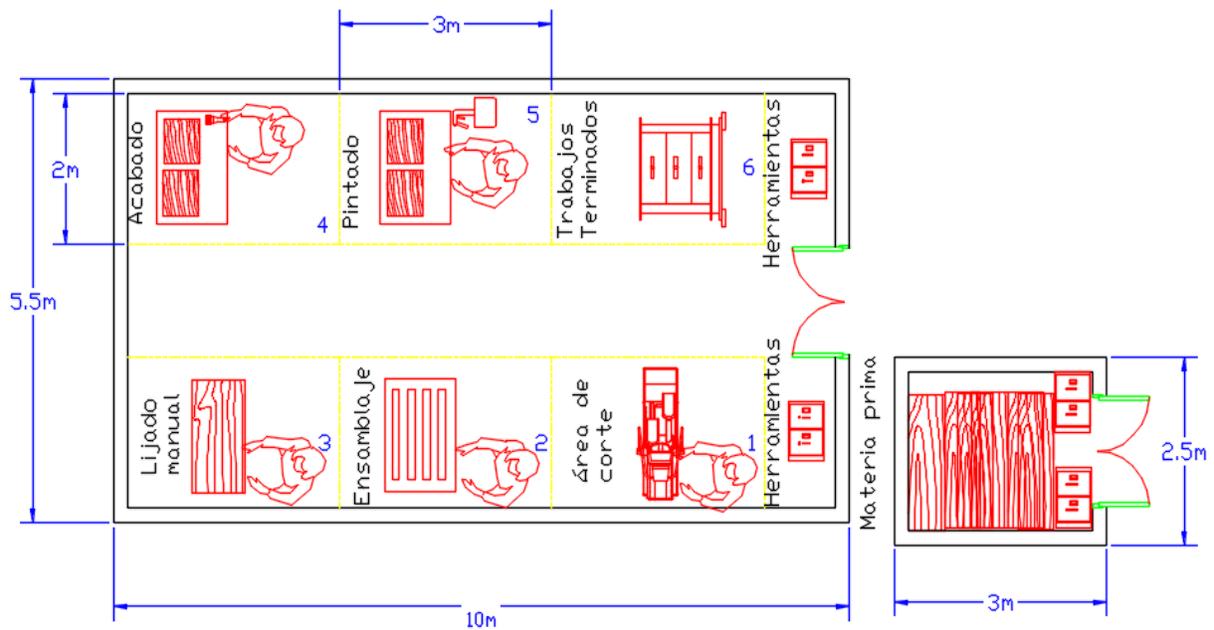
Distribución de planta propuesta para mueblería Alany. Fuente: Elaboración Propia.
